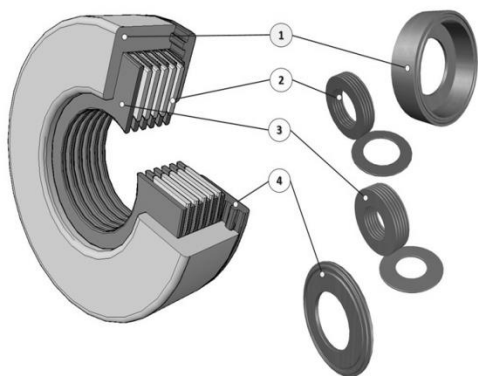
3D модель МЖУ: 1 – корпус, 2 – магнитоэластомерные шайбы, 3 - шайбы из немагнитного материала, 4 – крышка
